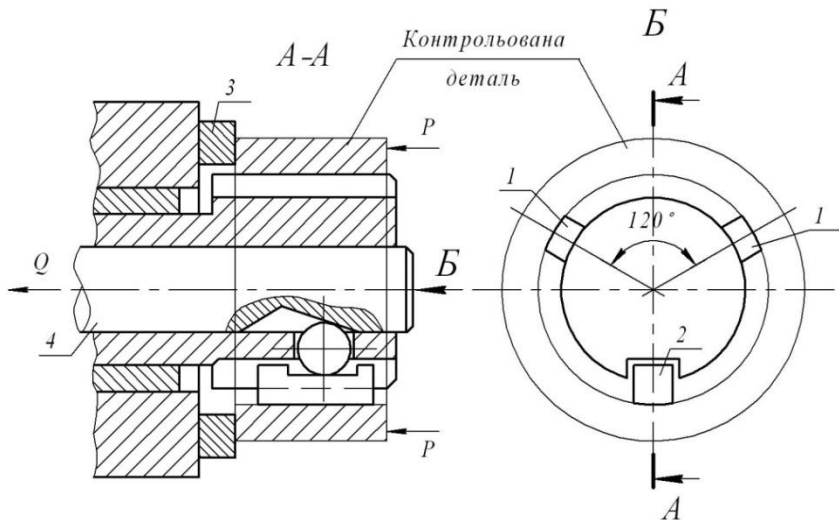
Схема установлення контрольованої деталі на розтискну оправку з двома нерухомими та одним рухомим кулачками
